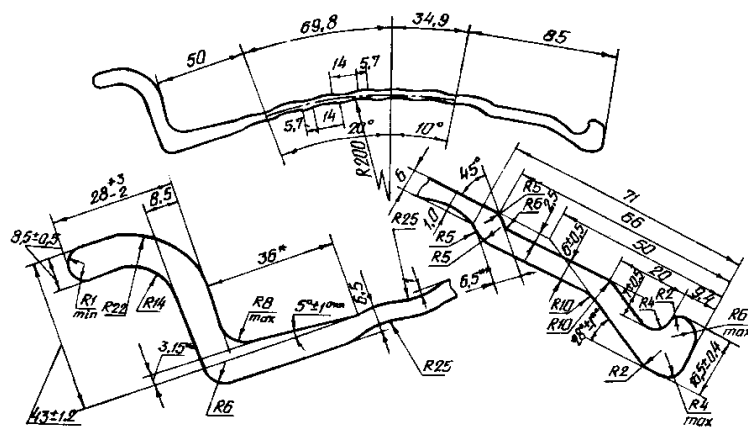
Рабочий чертеж профиля 8.5B-20-03
